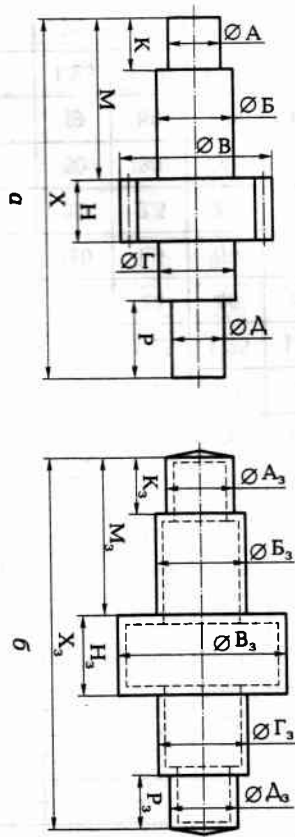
Эскиз обрабатываемого вала-шестерни:
